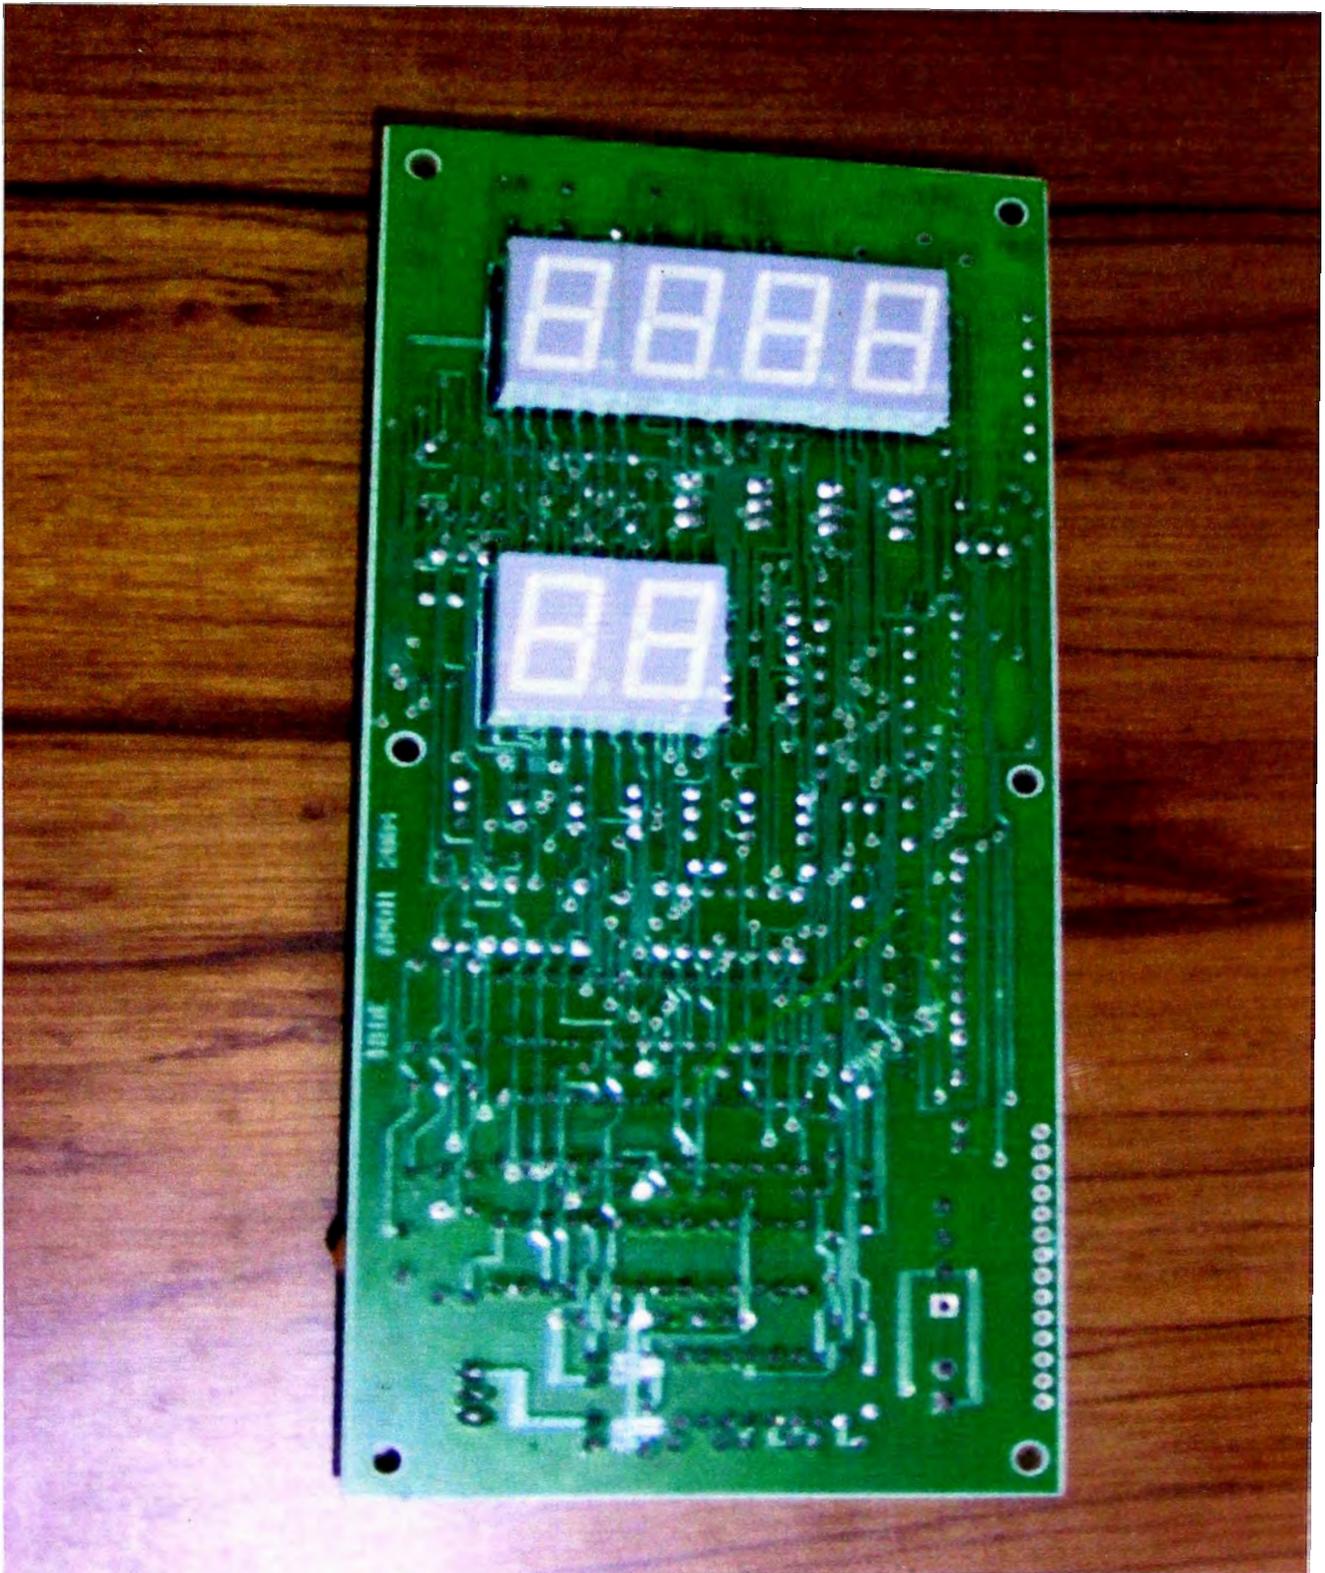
Tarjeta electrónica de Kit lado frontal.
